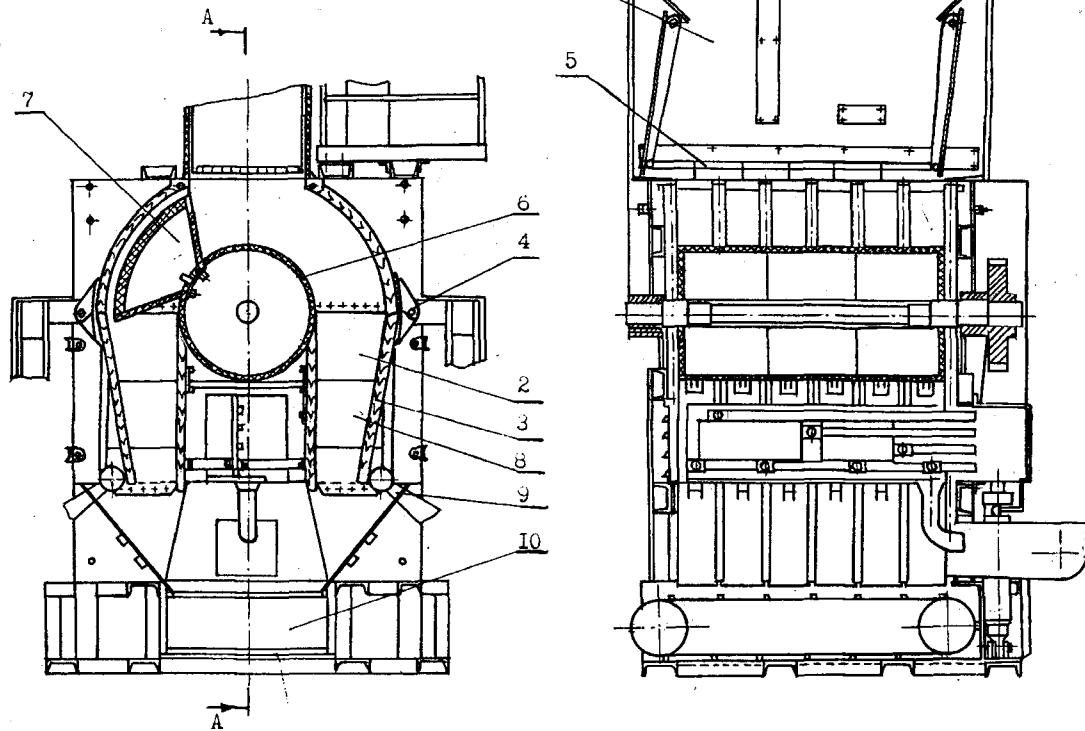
Конструктивная схема установки с решетчатым распределительным механизмом, вертикальными камерами и криволинейным ходом уплотнителя: 1 - бункер приемный; 2 - камера рабочая; 3 - стенка подвижная; 4 - шарнир; 5 - виброрешетка; 6 - барабан подвижный; 7 - уплотнитель; 8 - электроды; 9 - уплотнитель дополнительный; 10 - транспортер выгрузной.
